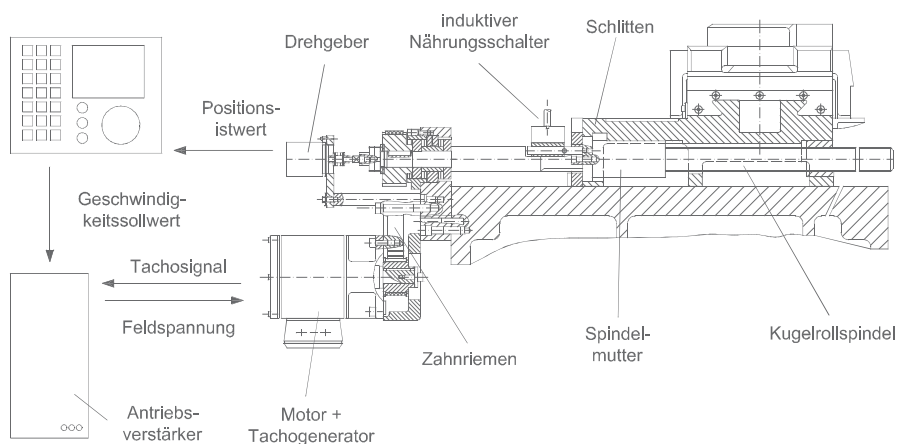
NC-gesteuerter Maschinenschlitten. Quelle: Boehringer
